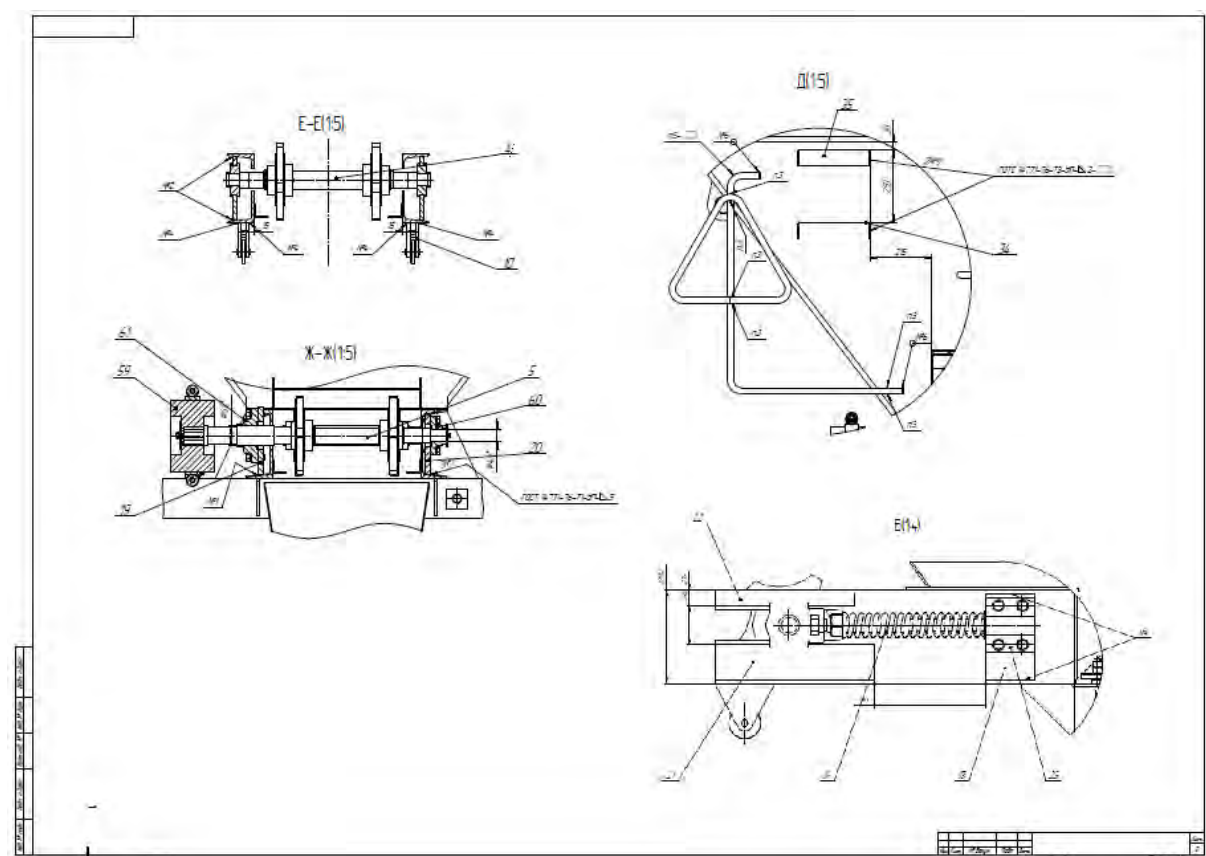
Сборочный чертеж бункера с пескоразбрасывателем
